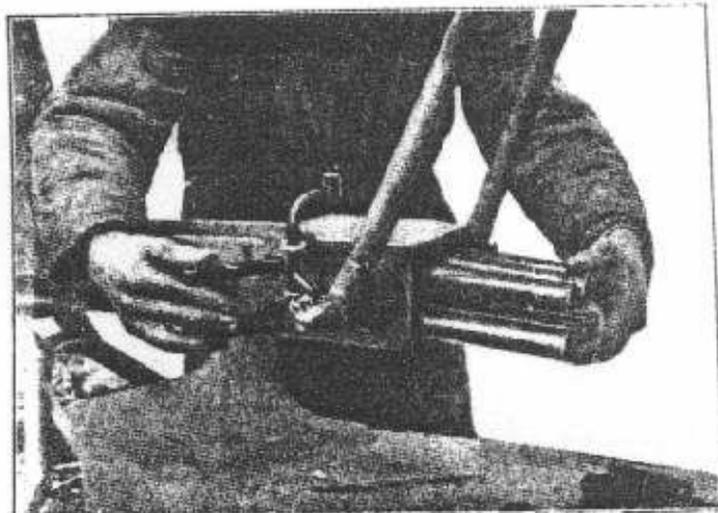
Come si levano le due cremagliere e il gruppo tubi reggi molla.
